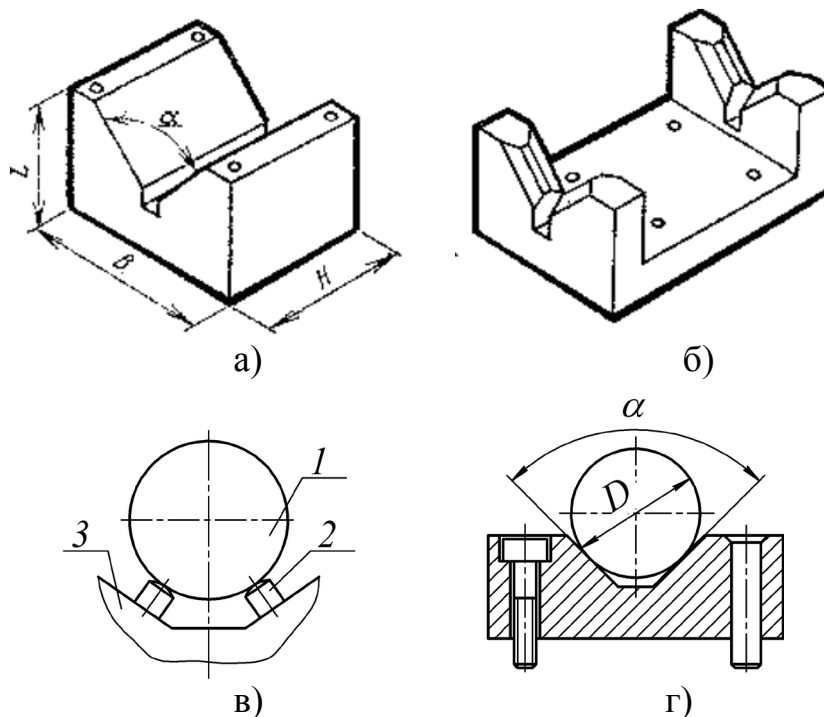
Типи призм і схема установлення заготовок у призми
